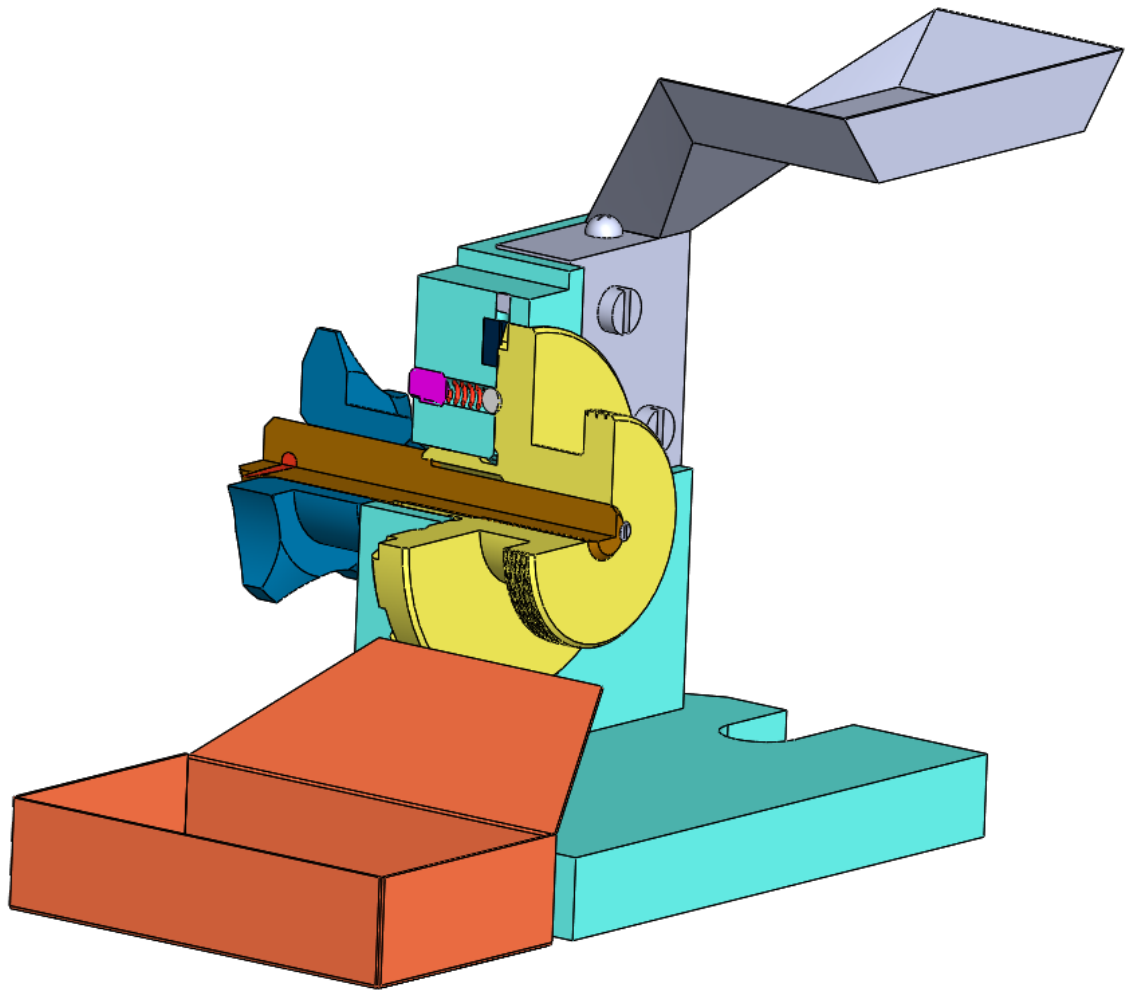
Кондуктор с бункерной загрузкой деталей (разрез).
